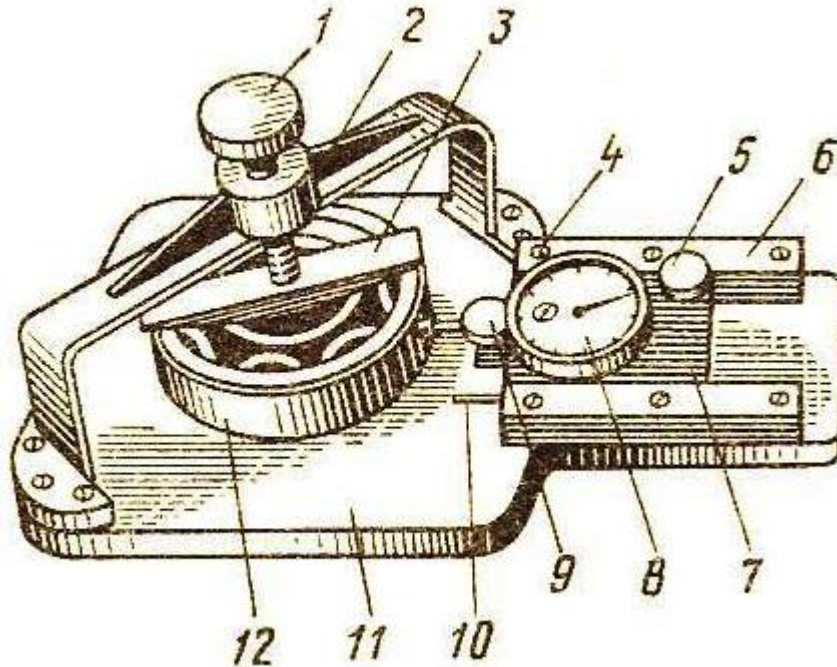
Прибор КИ-1223 для проверки радиальных зазоров в подшипниках качения.
